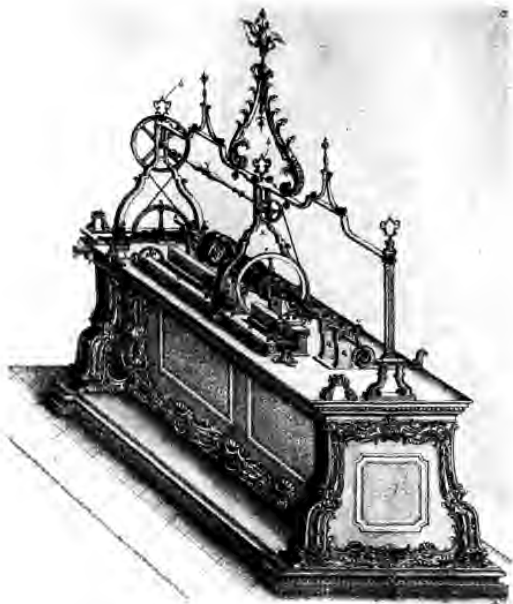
Токарно-копировальный станок. Рукопись «Театрум Махинарум»
